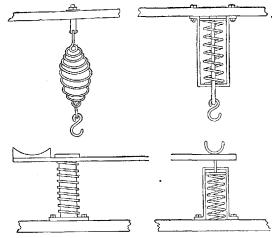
Различные типы подрессоривающих приспособлений с пружинными рессорами.
